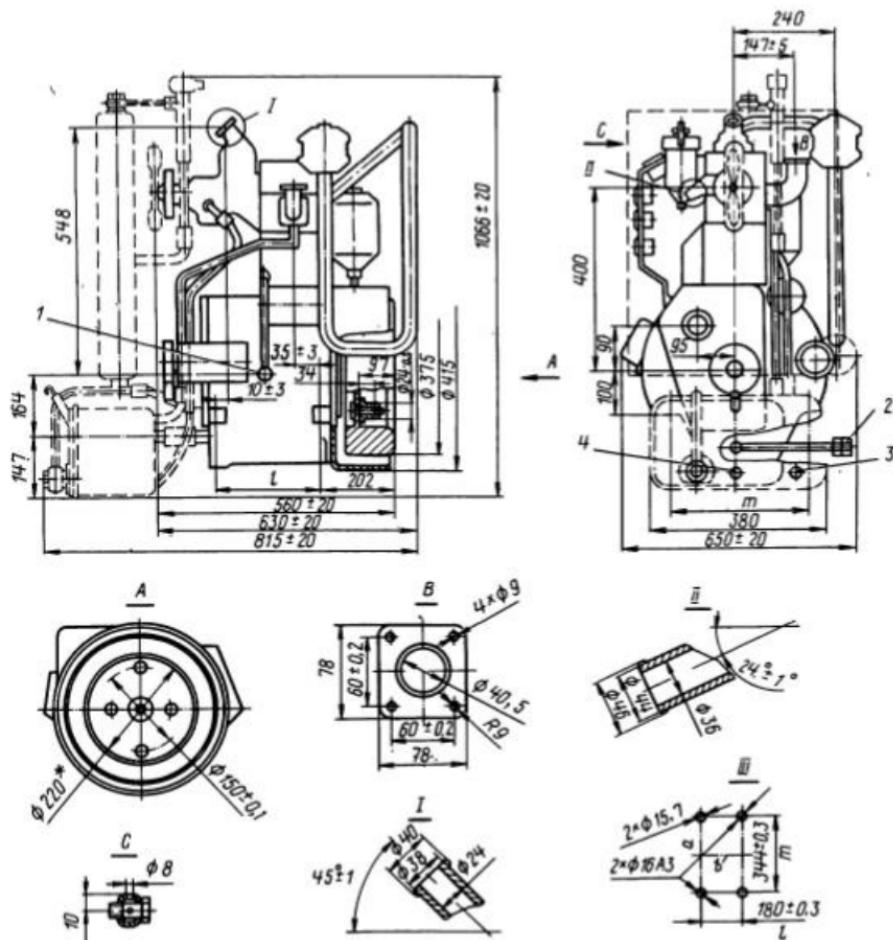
Габаритный чертеж дизеля ICh 8.5/11 (IP1-7P):
